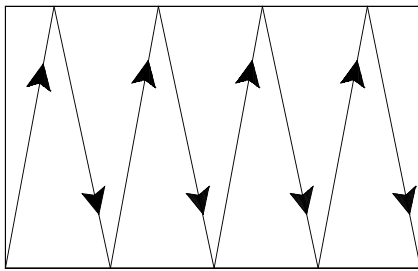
Схема перемещения оси инструмента по поверхности заготовки.
